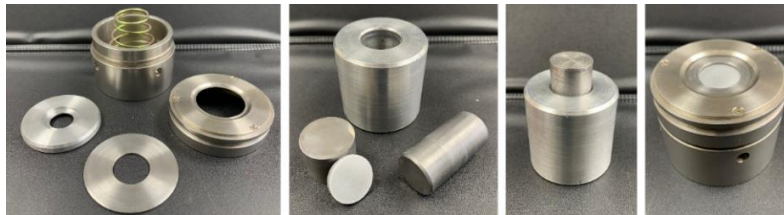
Molde de alumínio desenvolvido para realização do ensaio de FRX.
